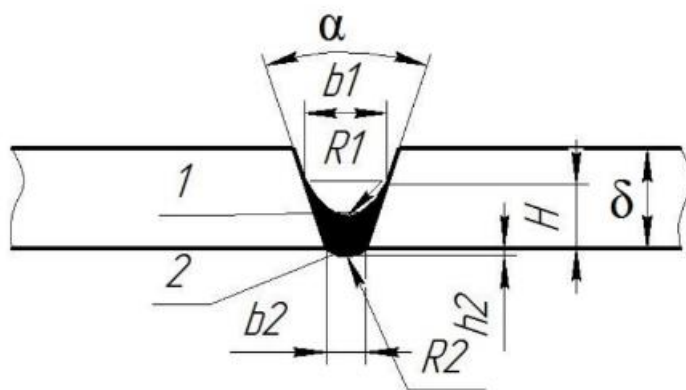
Геометрическая форма сварочной ванны при односторонней сварке с V-образной подготовкой кромок.
